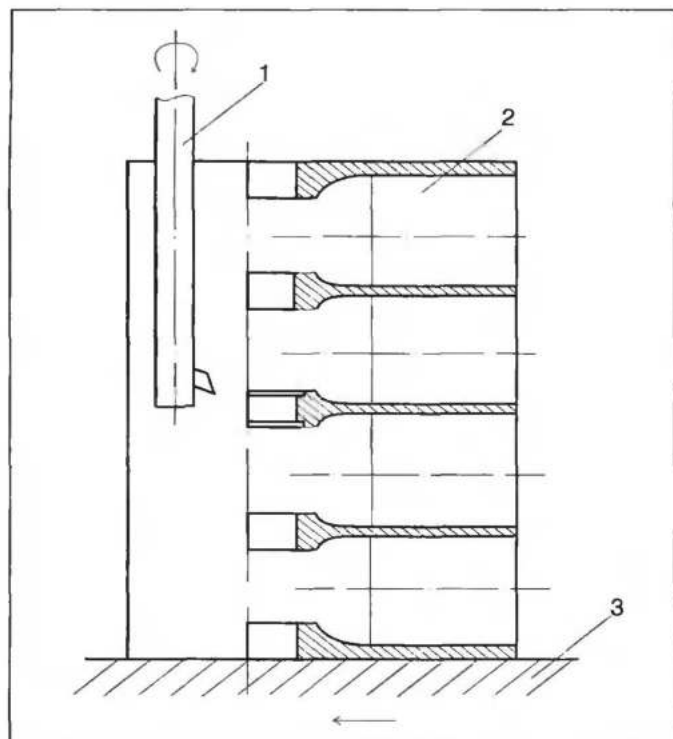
Схема растачивания упорных поверхностей на блоке цилиндров:
